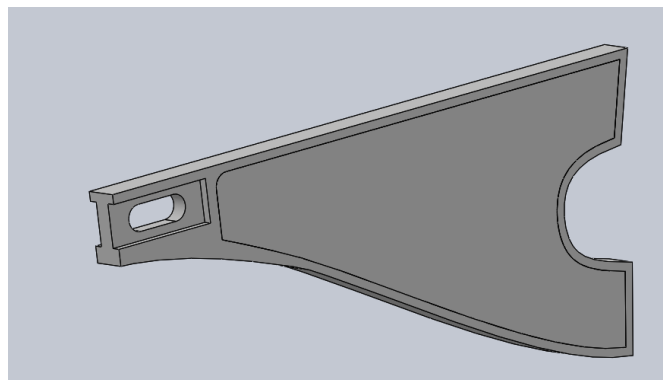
Vista del subensamblaje brazo izquierdo + chapa izquierda. [2]
